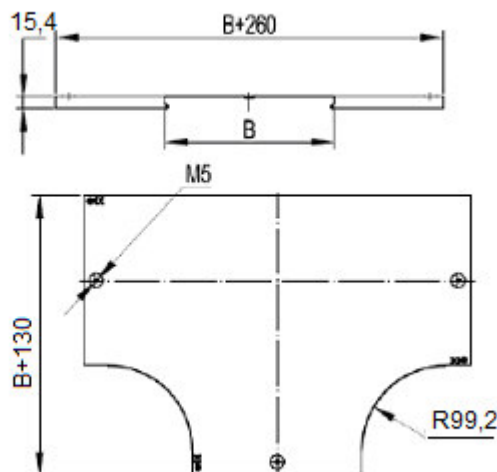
Крышка DPT на ответвитель Т-образный горизонтальный, тип 3804
